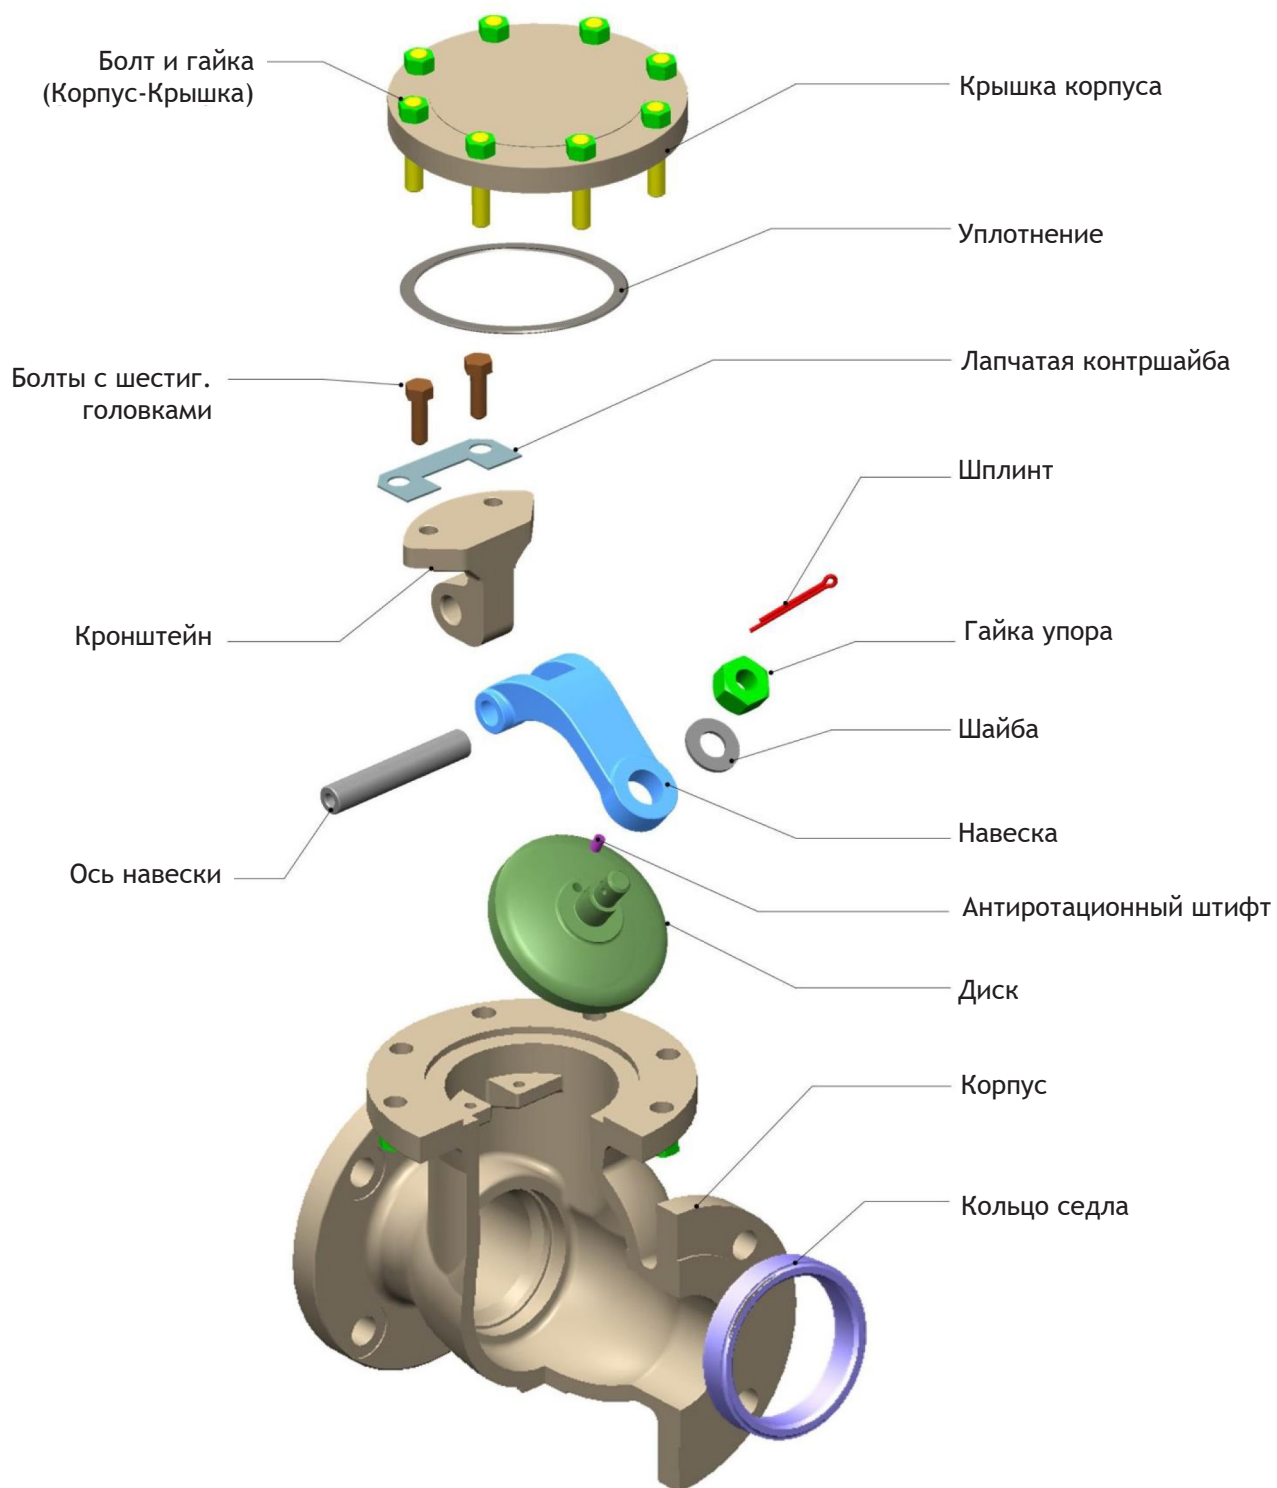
Поворотный обратный клапан (с внутренней навеской) - типовой
